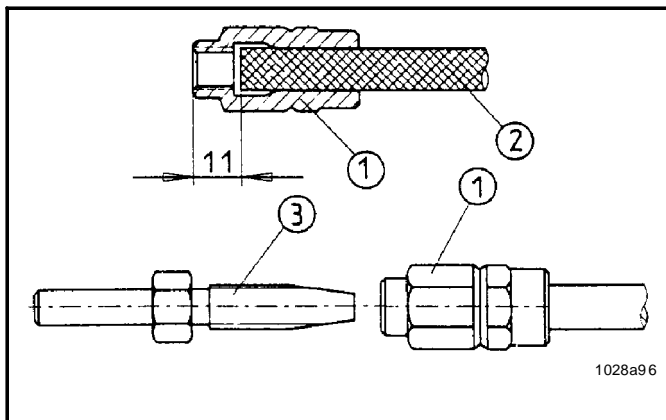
Premontaje del manguito roscado y tubuladura en el tubo flexible de plástico de alta presión
